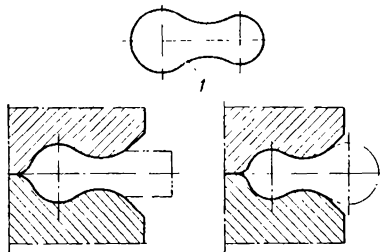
Два подкатных ручья для подкатки заготовки по частям: I — заготовка
